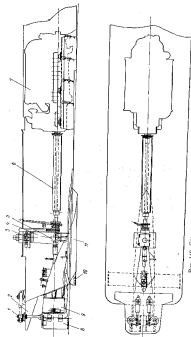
Схема установки вспомогательного двигателя на болтении катера.
